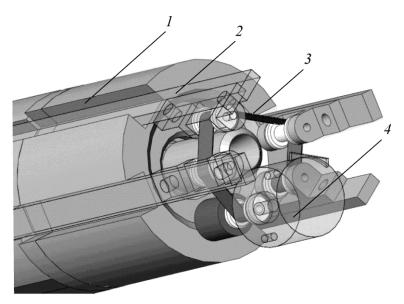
Схема установки энкодера и его соединения с планками: 1 — паз под планку; 2 — планка с роликом; 3 — струна; 4 — энкодер
